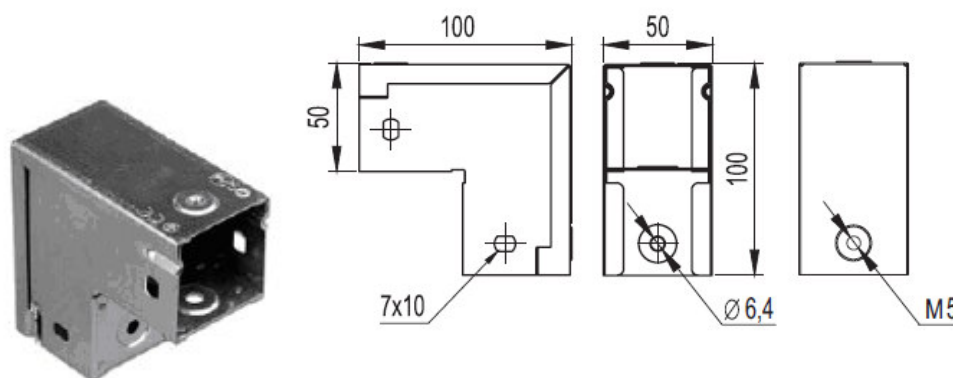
Угол вертикальный вниз 90° глухой, тип 39002
